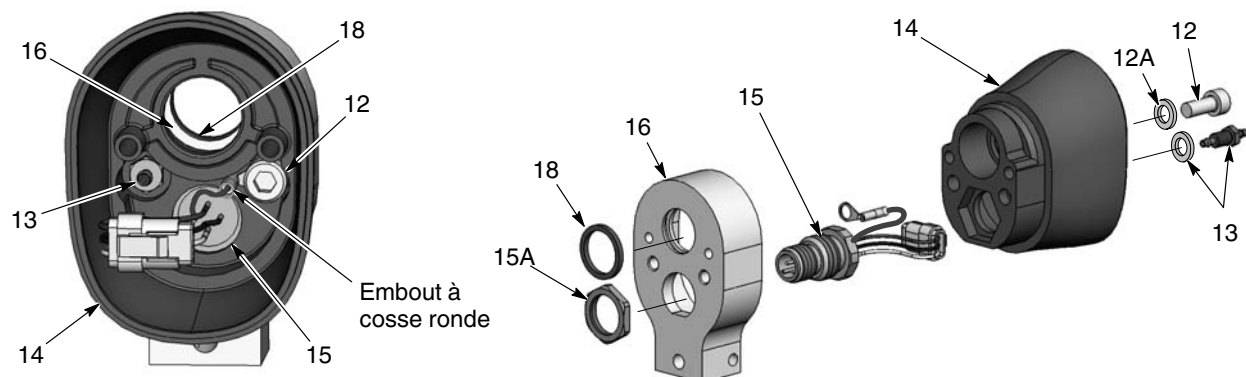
Démontage du pistolet à fixation sur barre 3 sur 3
